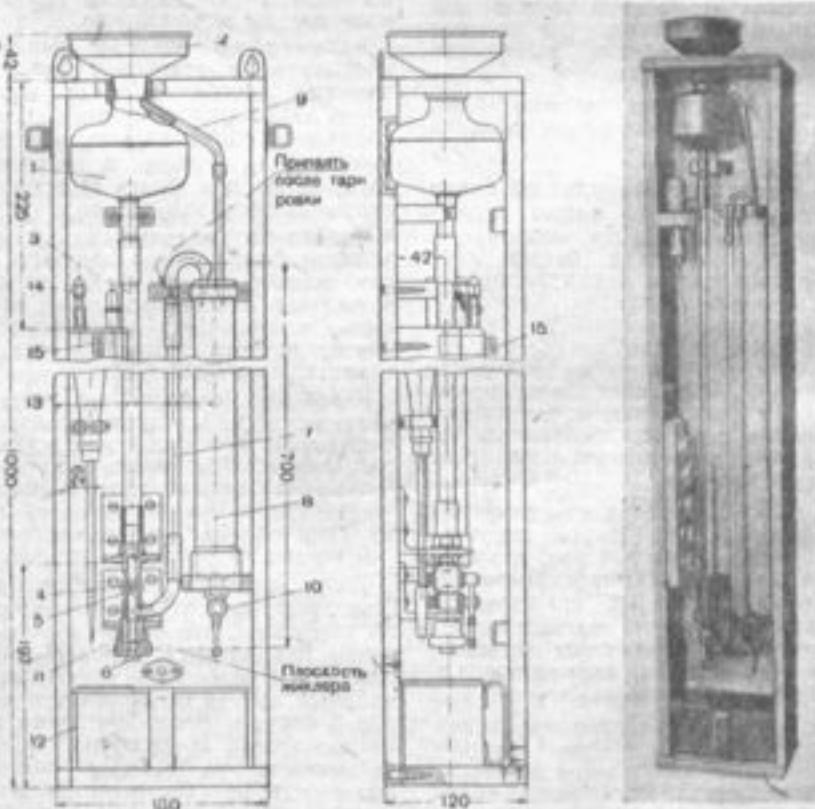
Сборочный чертеж прибора конструкции инж. П. Тарасова для проверки жиклеров
